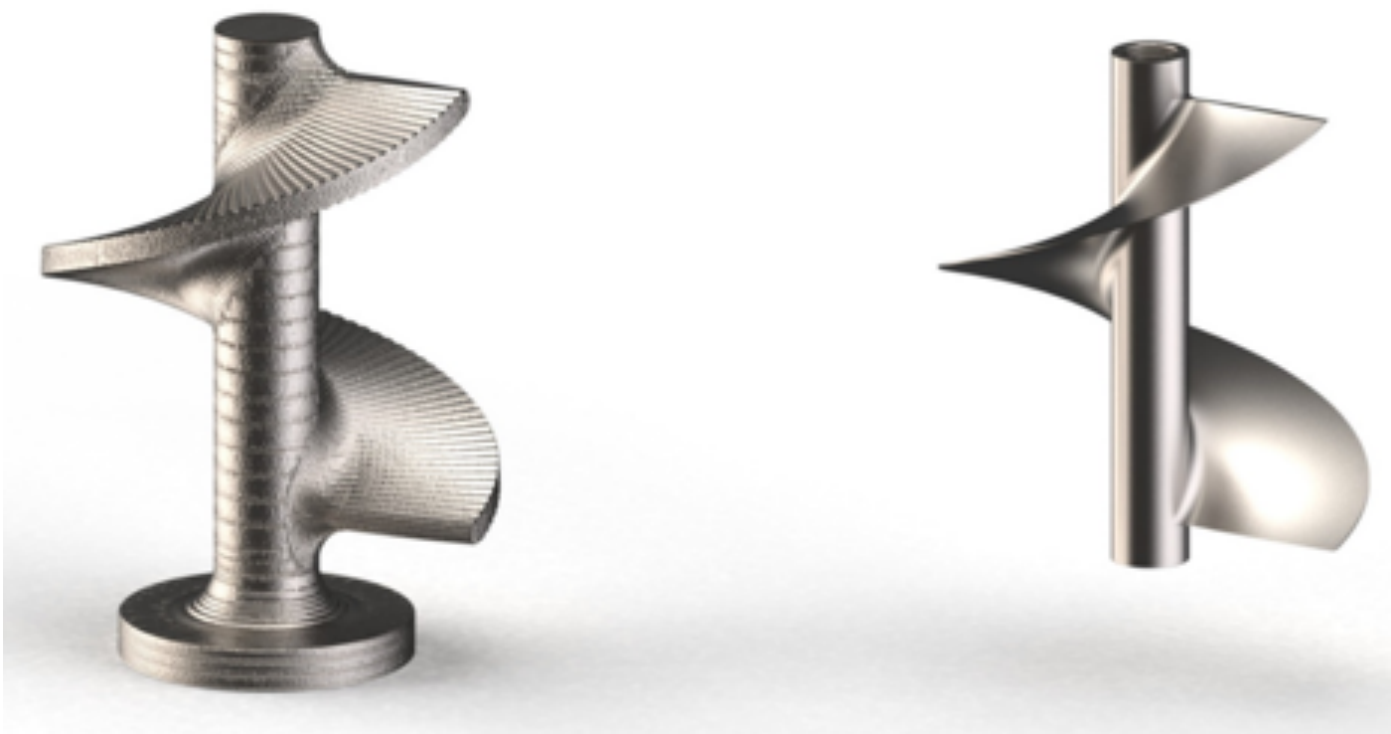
Выращенная заготовка для механической обработки (слева) и готовая деталь «Шнек» (справа)
